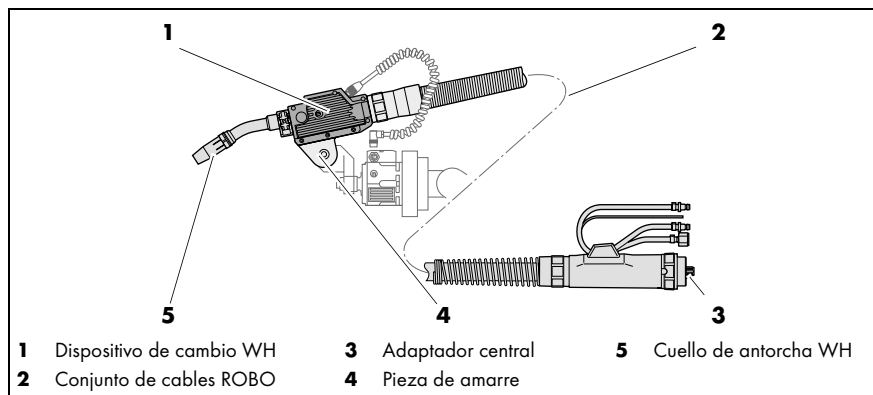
Antorcha de soldadura WH/WHPP
